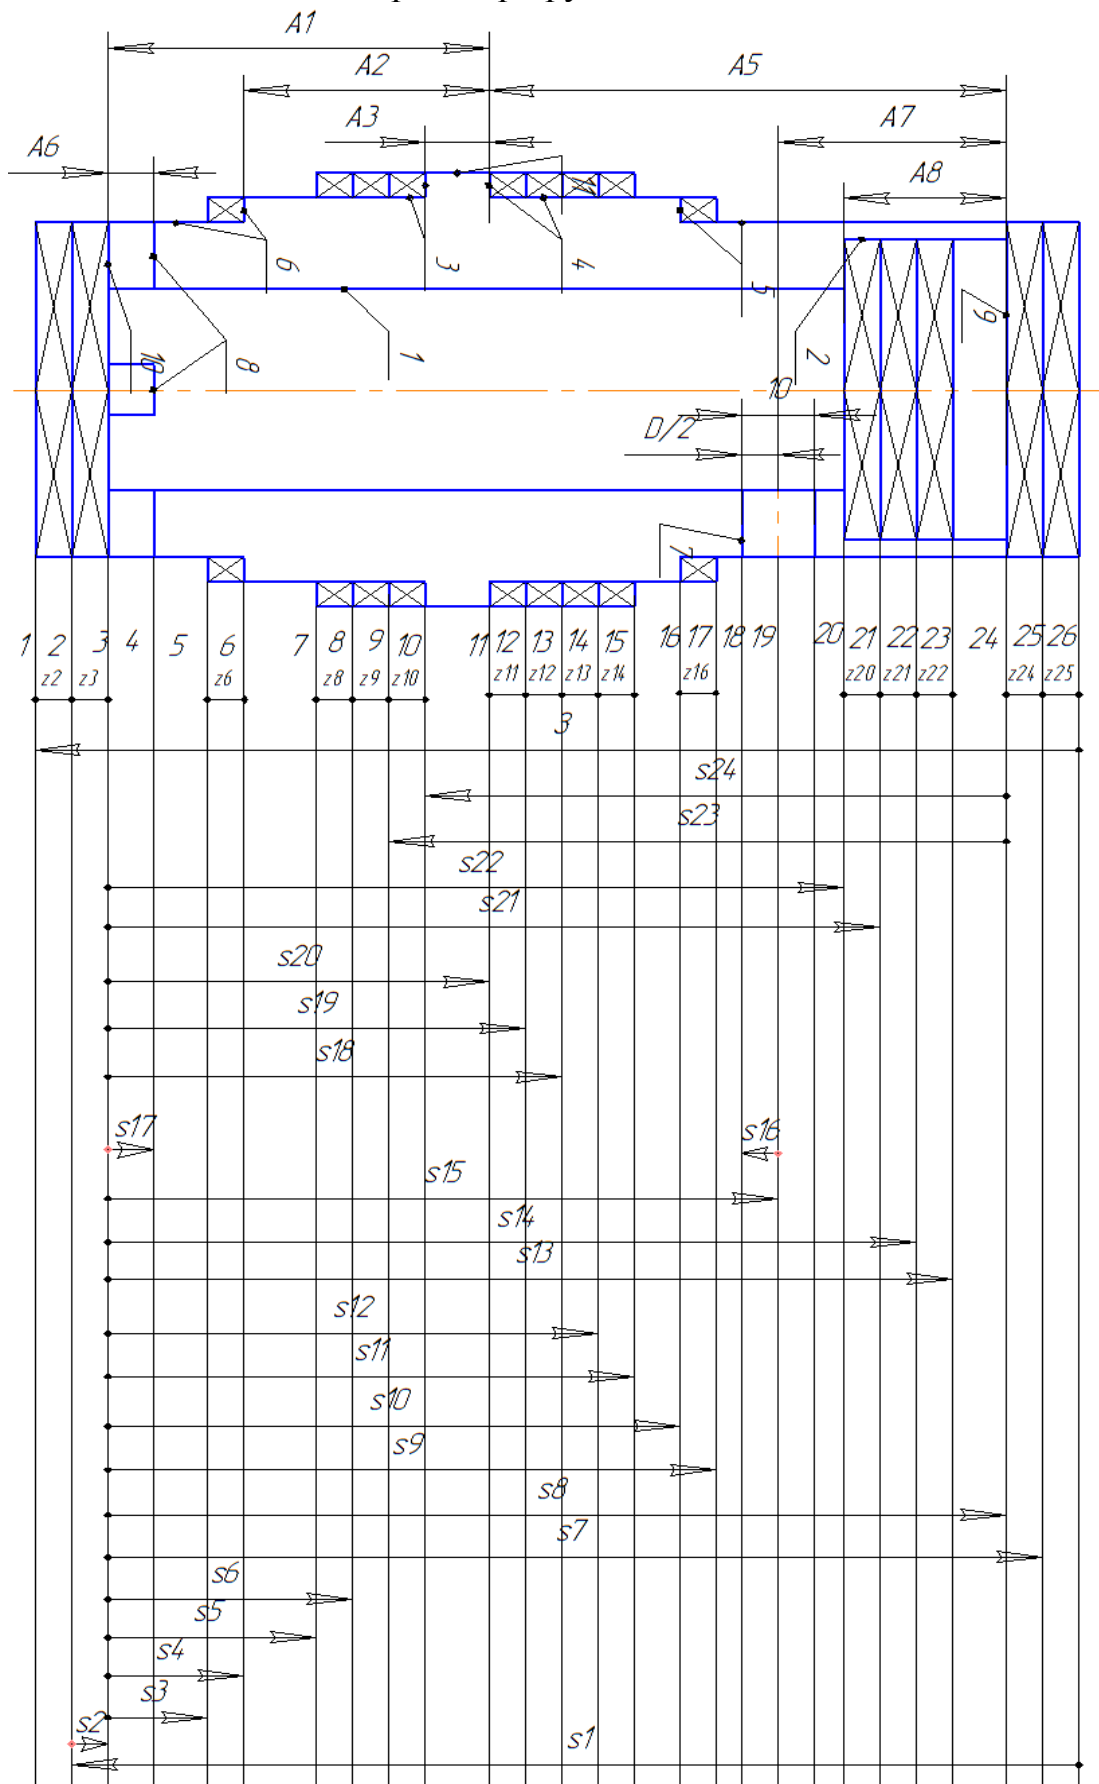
Размерная схема второго маршрута изготовления детали
